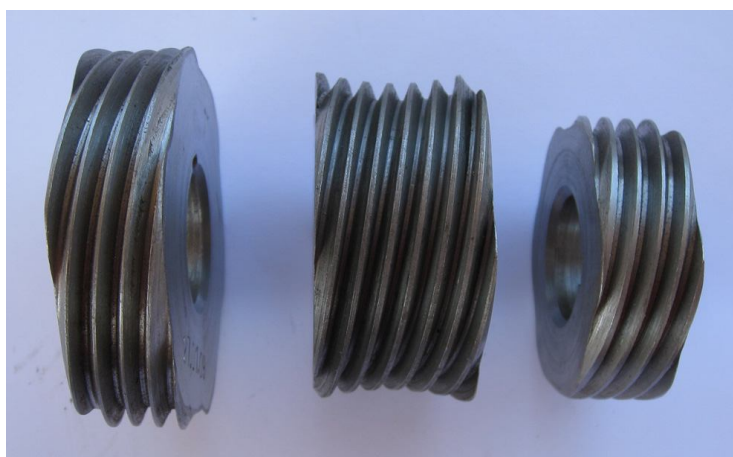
Шестизаходные гиперболоидные зубчатые колеса
